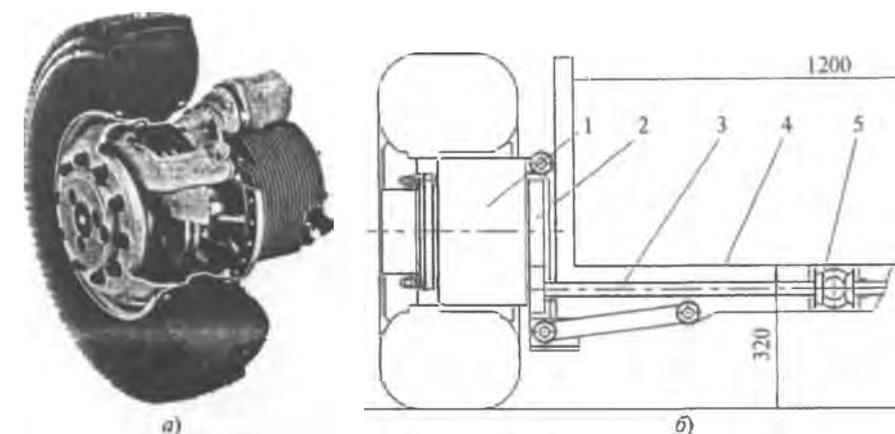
Мотор-колесо для транспортных машин (а) и схема компоновки автобуса с колесным вариатором (б):
